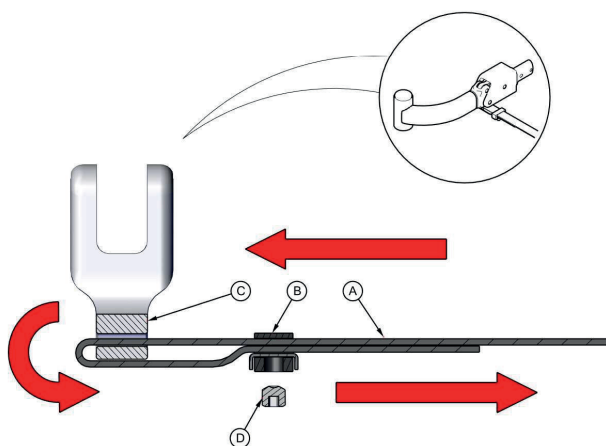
Installer la courroie du mécanisme de fourches escamotables
